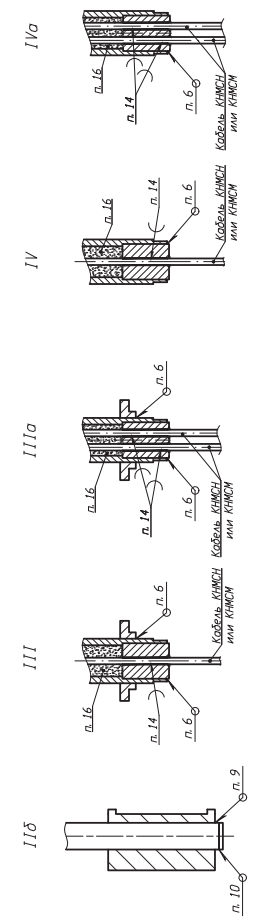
Чертеж средств взрывозащиты. Варианты исполнения защитного корпуса ТС(ТС.К, ТС.П)-Exd(Exdi)
